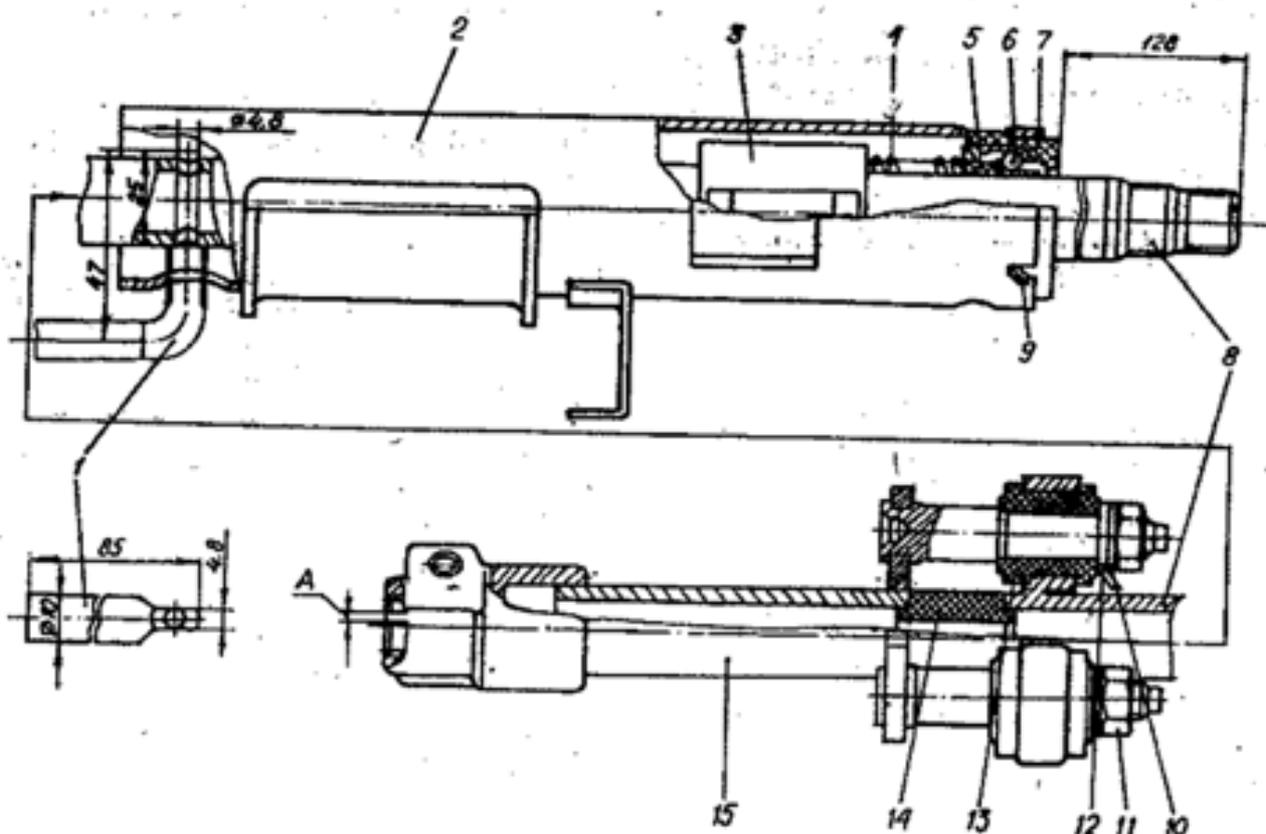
Опора вала в сборе: 1 - технологическая деталь, устанавливаемая при сборке в вал и опору; 2 - опора вала; 3 - кольцо запорное противоутоного устройства; 4 - пружина; 5 - упор подшипника; 6 - подшипник; 7 - втулка опорная; 8 - вал верхний; 9 - выступ на опоре вала (ограничитель глубины установки переключателя на опору); 10 - шайба; 11 - гайка; 12 - контакт массовый; 13 - втулка муфты; 14 - буфер; 15 - вал нижний.
